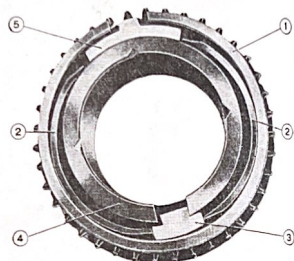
Sincronizador sobre el engranaje de Tercera.
